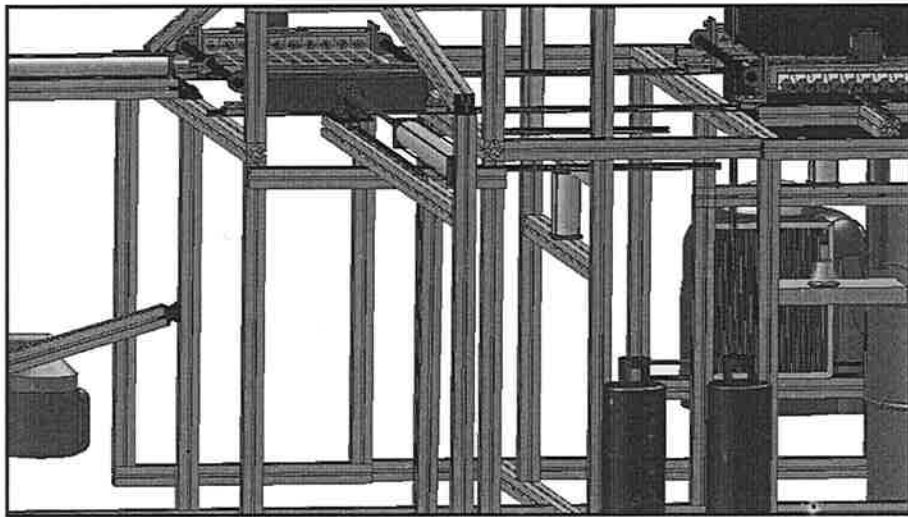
Ensamble de estructura en la cara frontal de la máquina.
